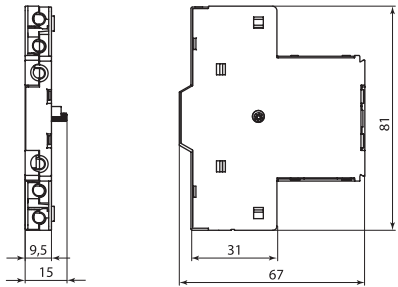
Габаритные и установочные размеры дополнительных и аварийных контактов ПРК32.
